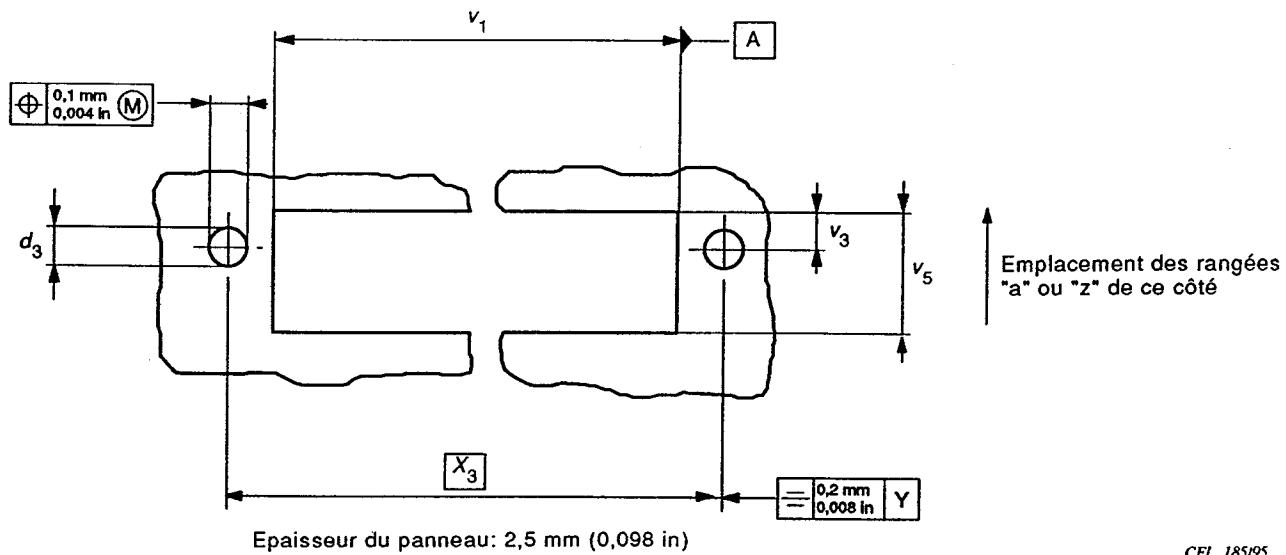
Panneau d'essai (pour l'essai de tension de tenue)
